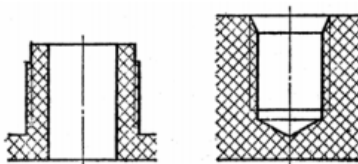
Конструкція зовнішньої і внутрішньої різей, які формуються при пресуванні
